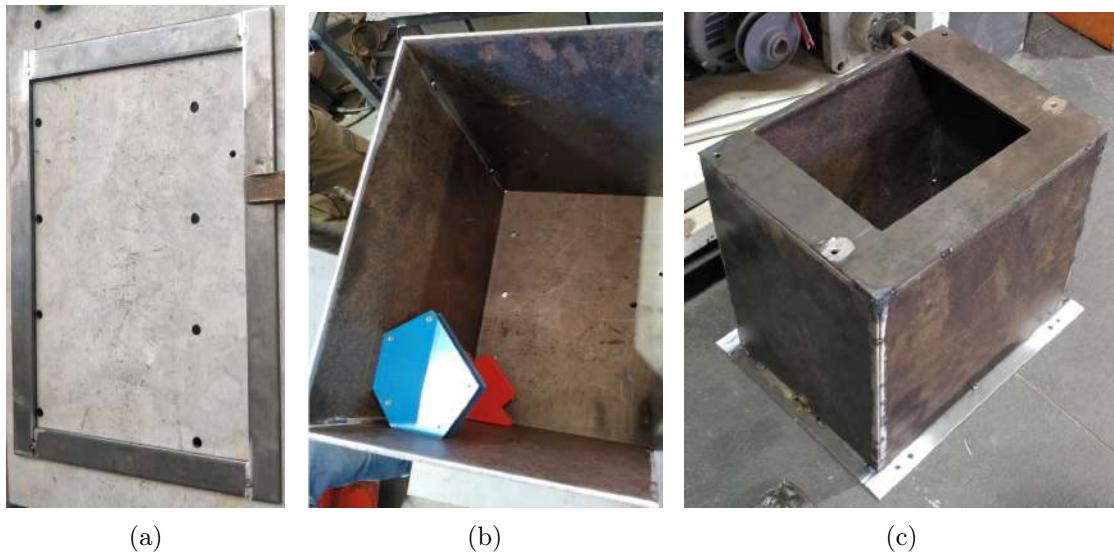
Processo de soldadura do espaçador: (a) Soldadura da chapa de baixo (b) Soldadura das chapas laterais, (c) Componente final.
